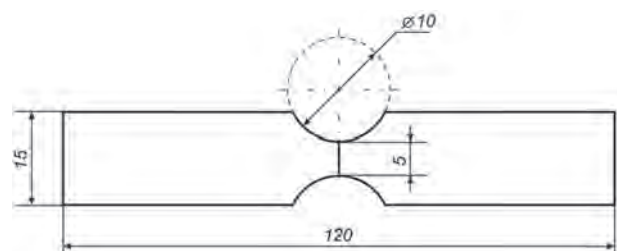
Образец для испытаний сварного соединения на разрыв
